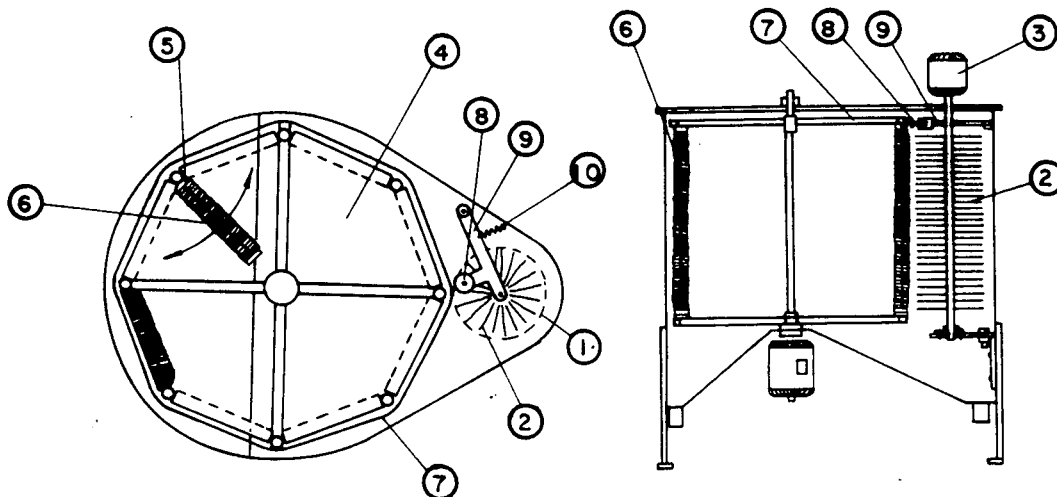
Máquina desoperculadora e extratora formando conjunto único [16].
